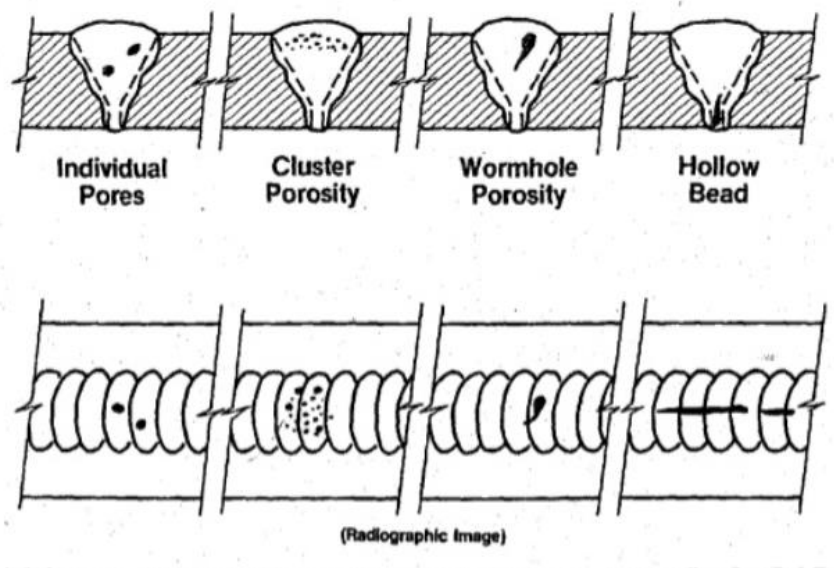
Tipos de porosidades que se encuentran en un cordón de soldadura.
